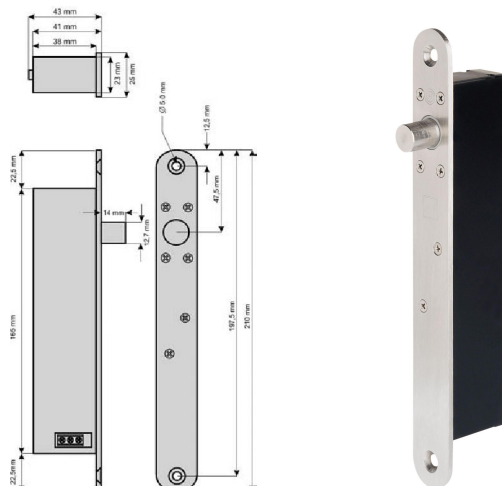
Elektromagnetický zámek s klínovou západkou Technilock L3/M4
